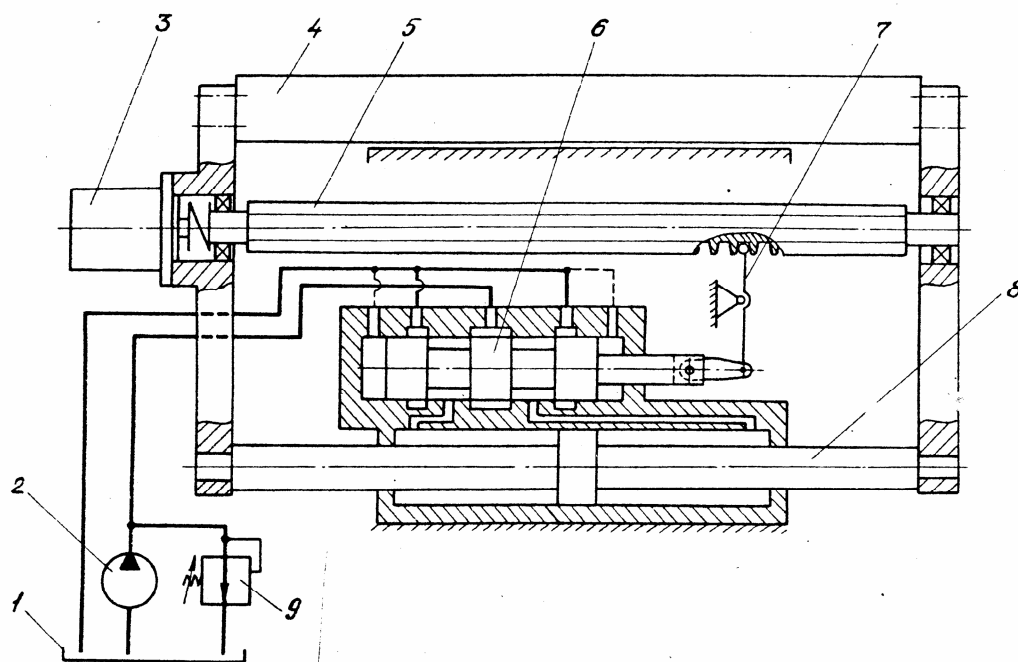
Схема привода подачі багатоцільового верстата ЛТ260МФ3
